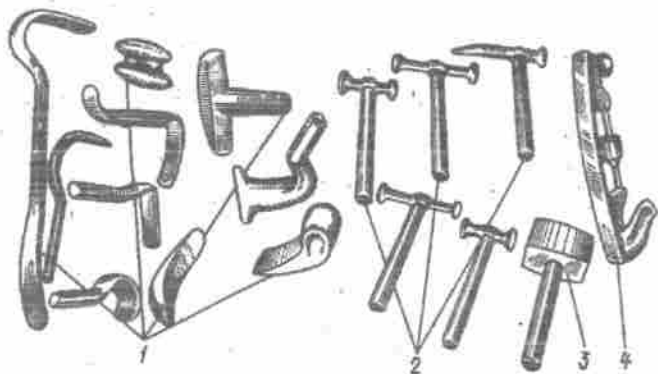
Werkzeugsatz zum Richten von Karosserie und Kabine:
